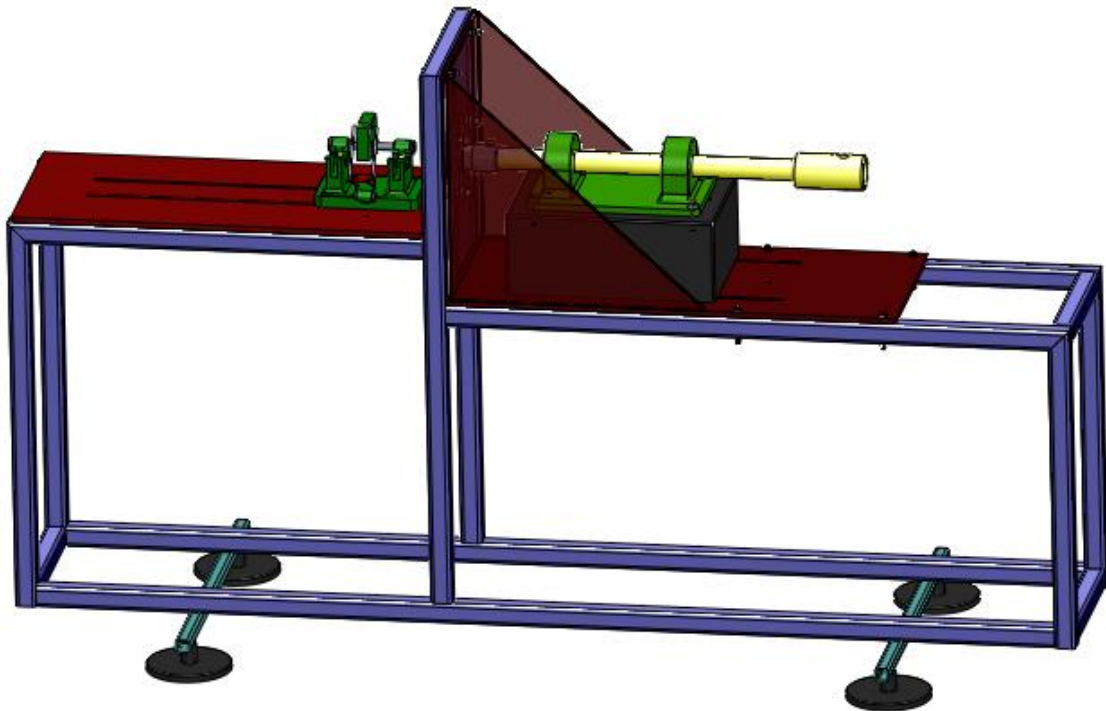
Modelo en 3D del prototipo de máquina para expandir tubos.
